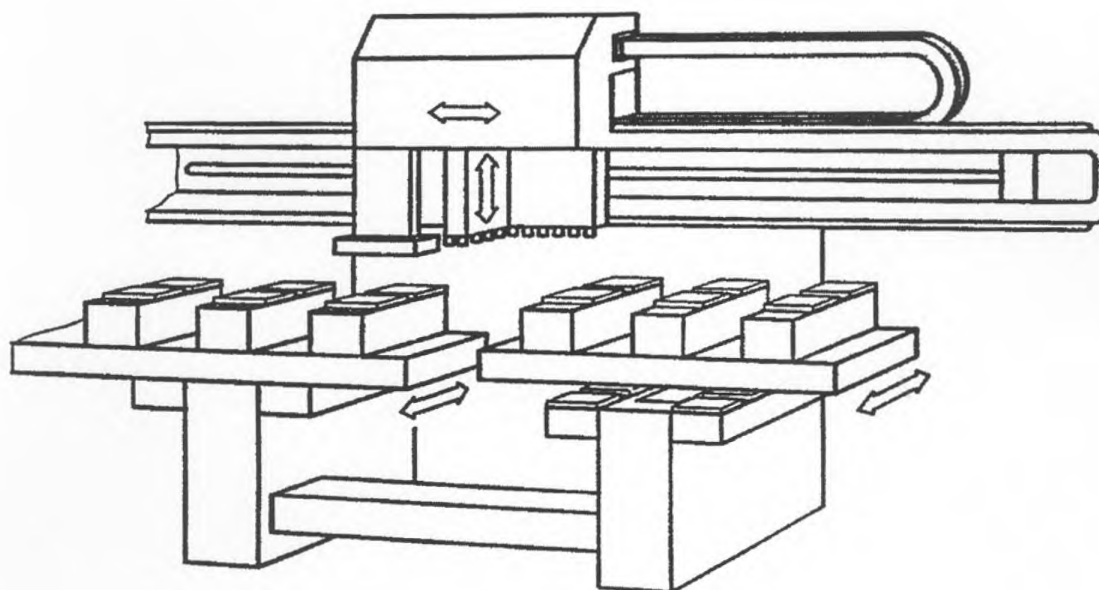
Сверлильный станок с каркасом в виде буквы С (подвижный стол, неподвижный портал, подвижная головка)¹
